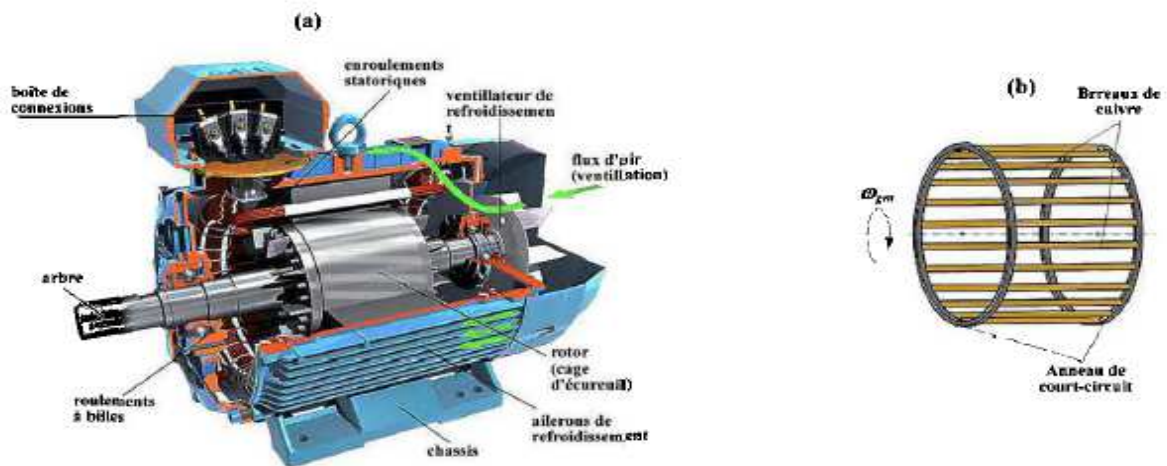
La machine asynchrone: (a) constitution; (b) la cage d'écureuil.
